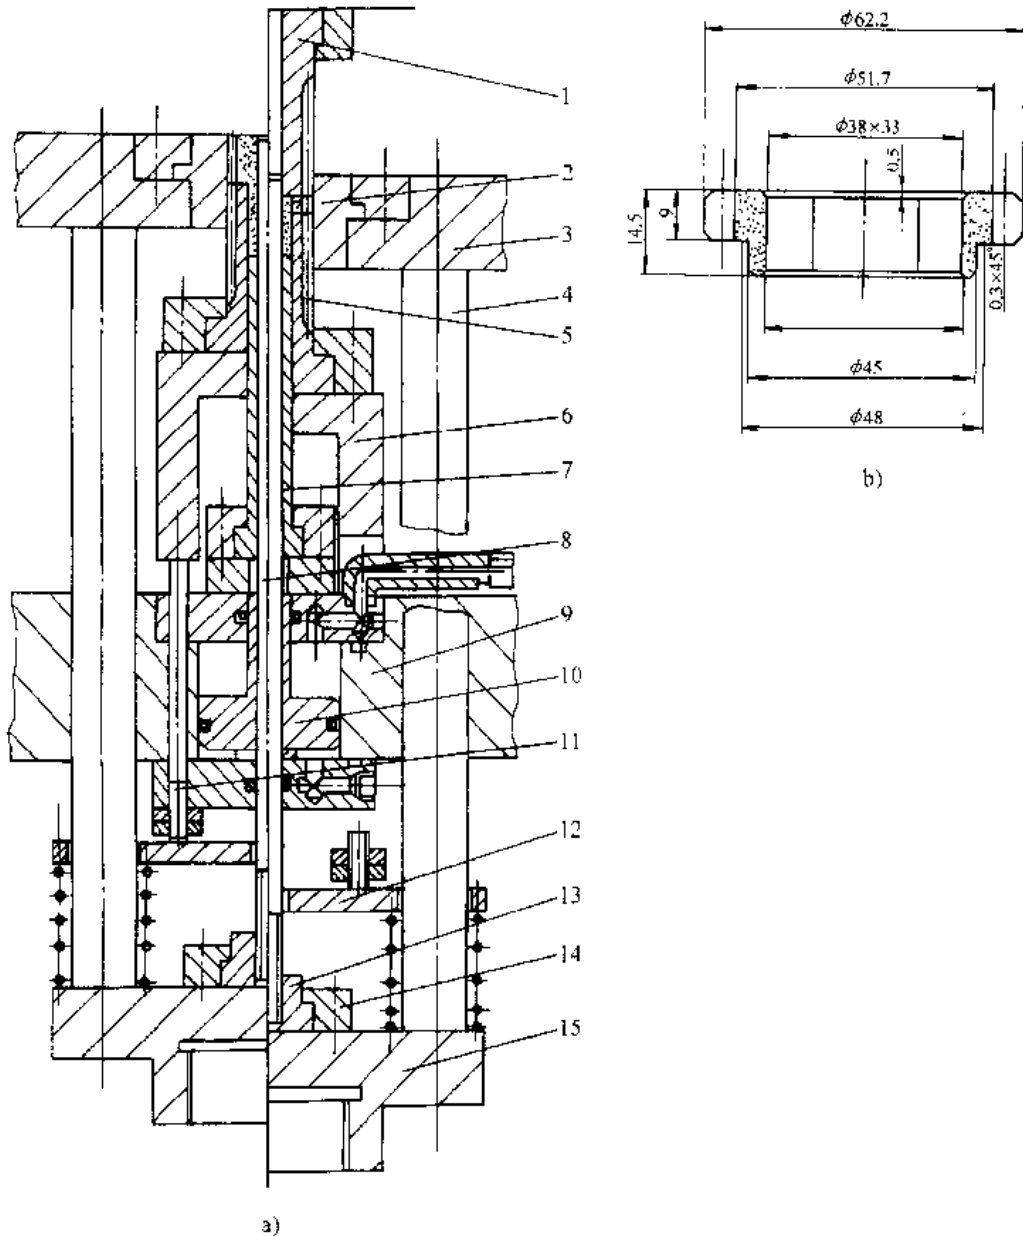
压制带台阶面的油泵外齿轮压坯的成形模具
